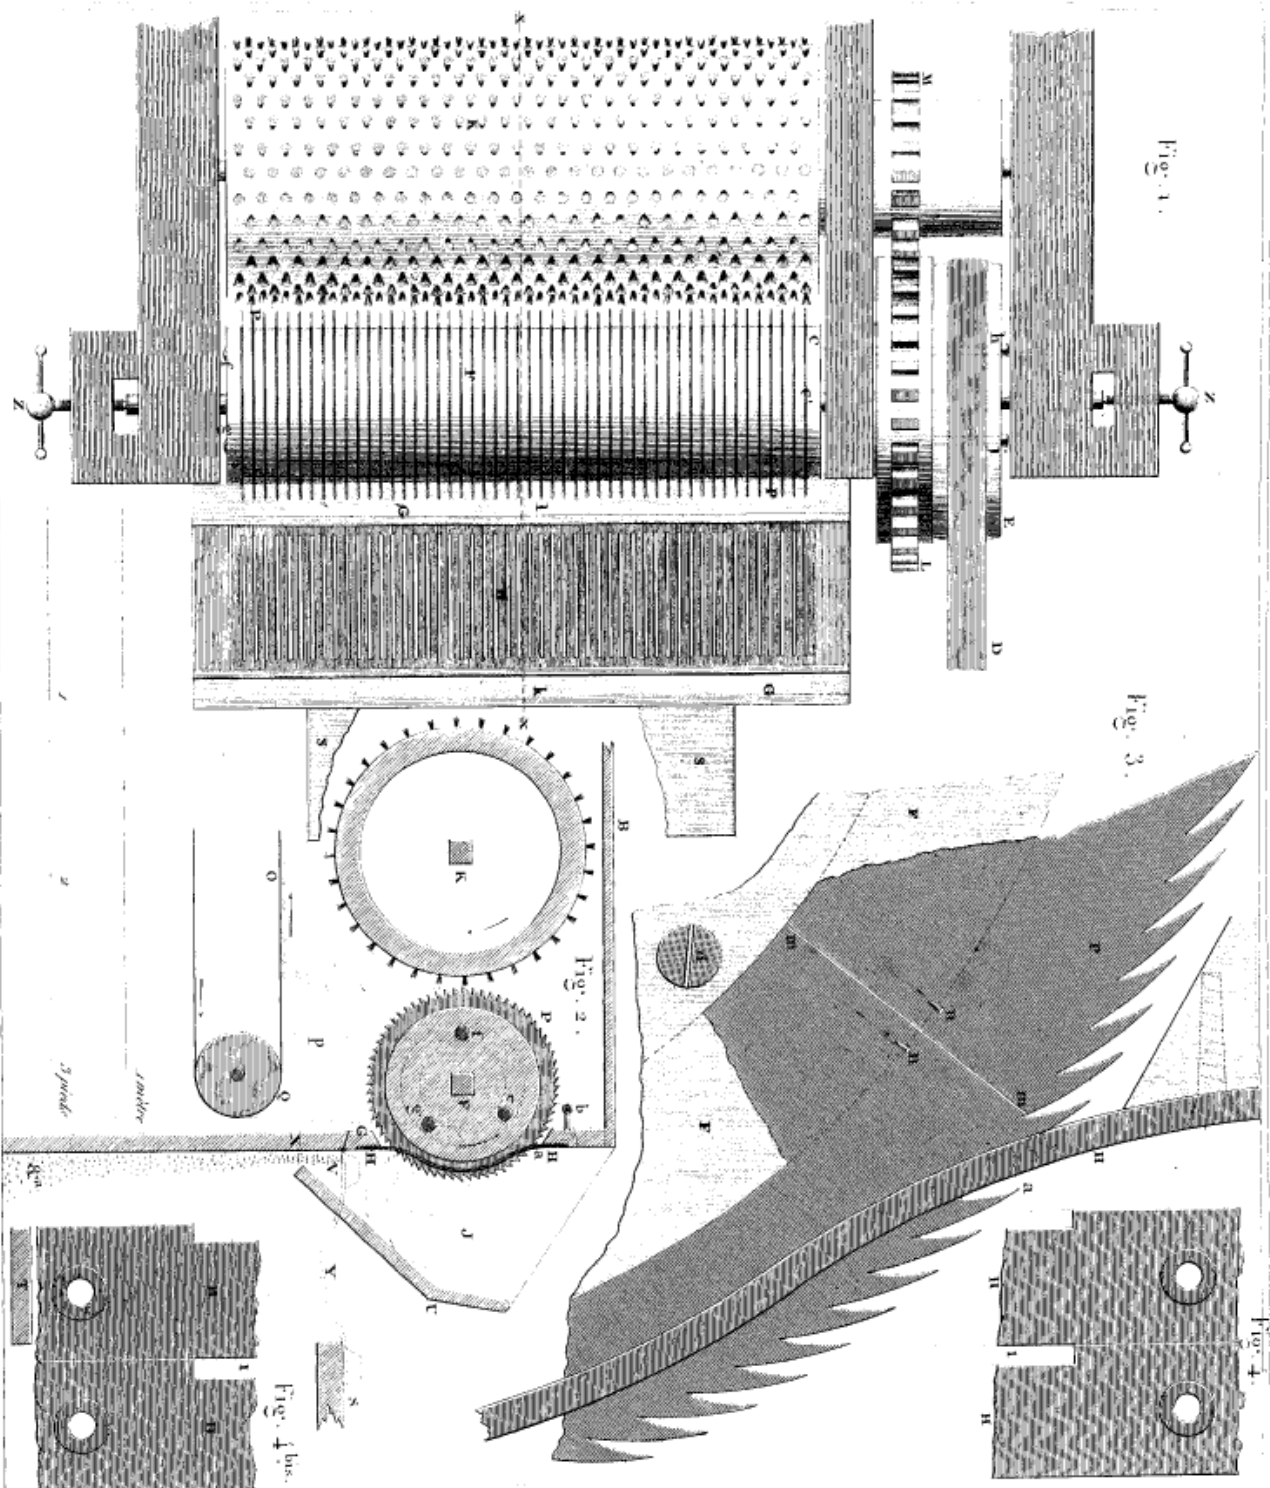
Plan du moulin, le plancher B étant enlevé, et le cadre G des barreaux H étant abaissé.
